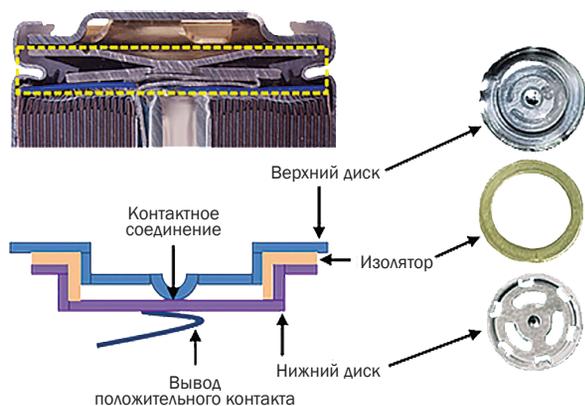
Общий вид и схема устройства прерывания тока «CID»
